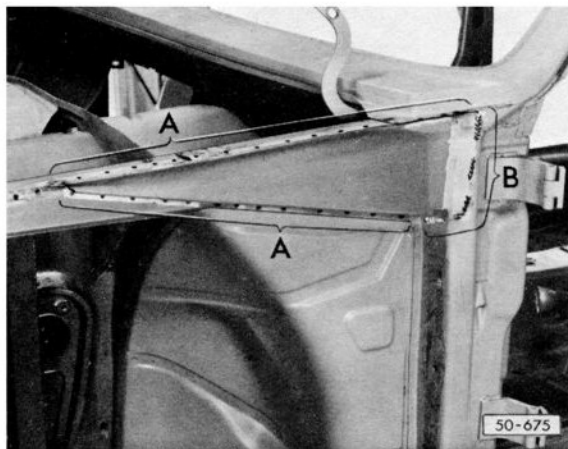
Aufbau-Vorderteil-Teilstück einschweißen
